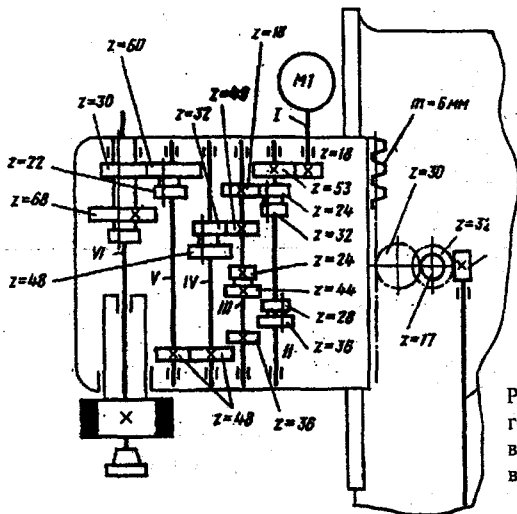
Кінематична схема головного приводу вертикально-фрезерного верстата мод. 6А54
